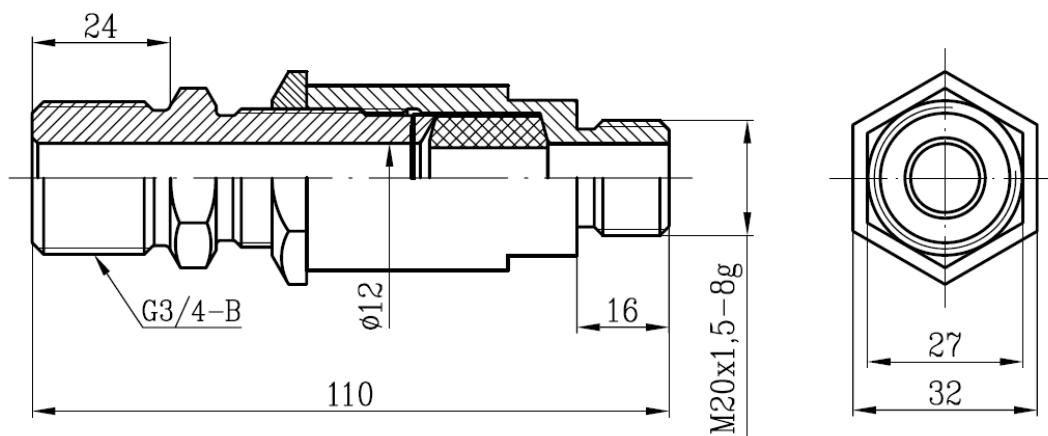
Ввод кабельный для трубного монтажа (ТБ 3/4")
